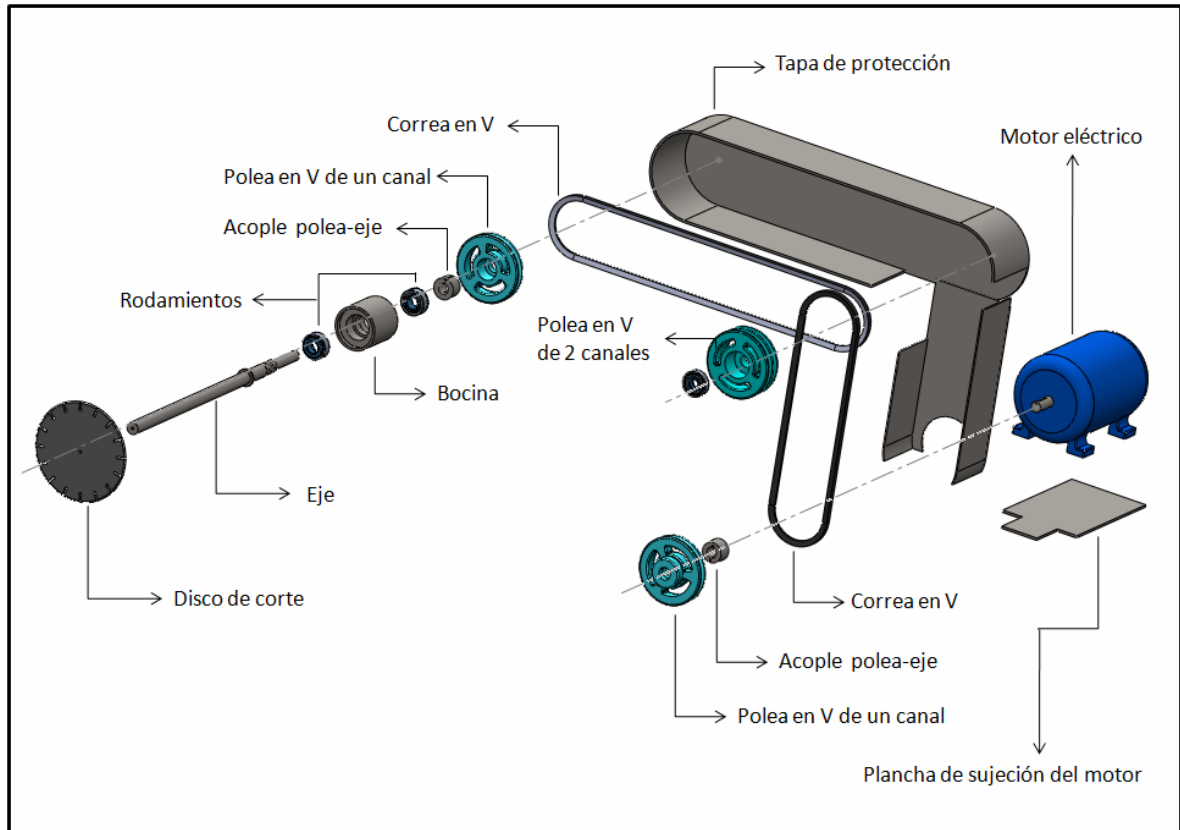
Despiece del mecanismo de corte ^[Fuente: propio].
